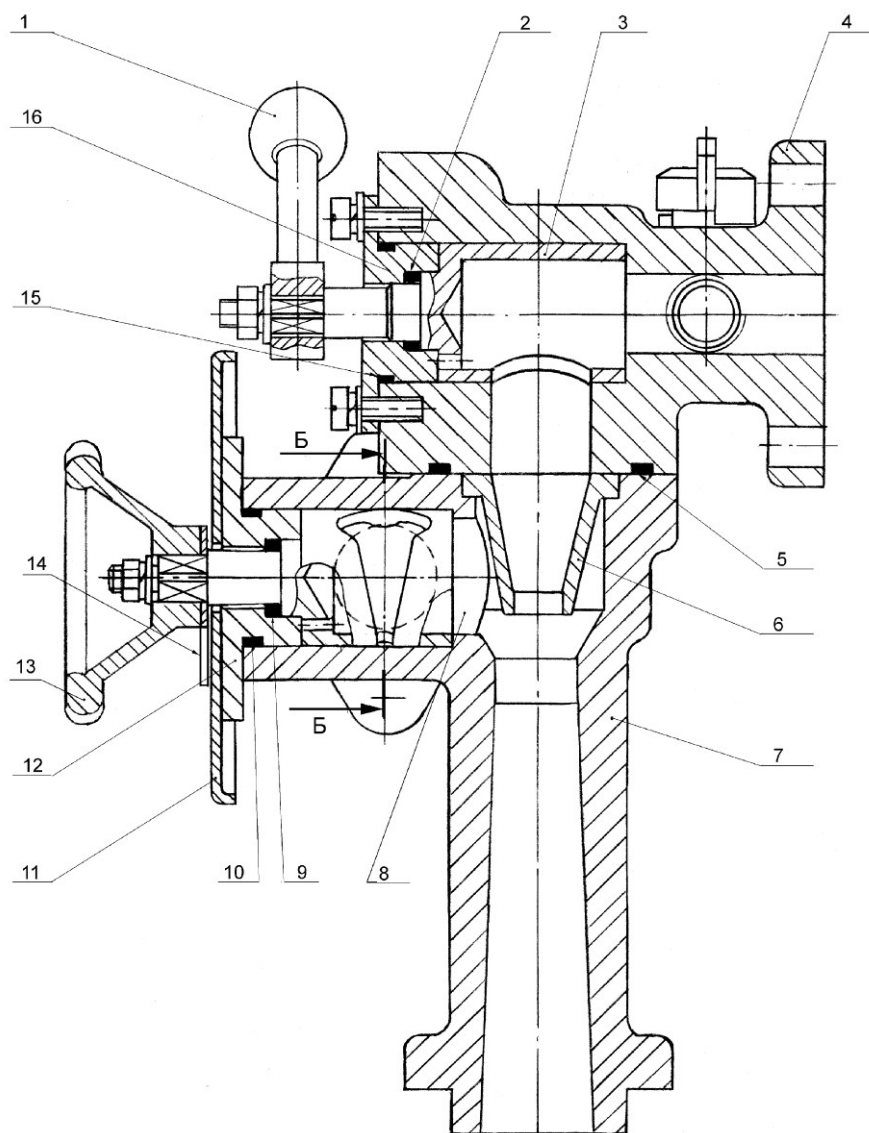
Рис. 5. Пеносмеситель НЦПВ-20/200: 1 – рукоятка крана эжектора; 2, 5, 9, 10, 15 - кольца уплотнительные; 3 – пробка крана; 4 - корпус крана; 6 – сопло; 7 – корпус пеносмесителя; 8 – дозатор; 11 – крышка; 12 – крышка дозатора; 13 - маховик; 14 – стрелка; 16 – крышка крана.
